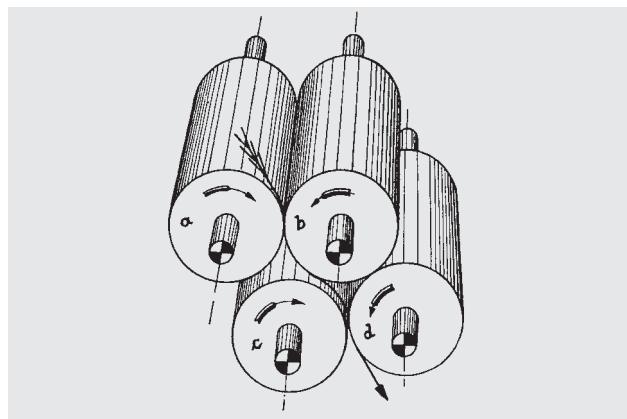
Vierläuferwalzwerk mit vier Walzen für dreimaligen Materialdurchgang
